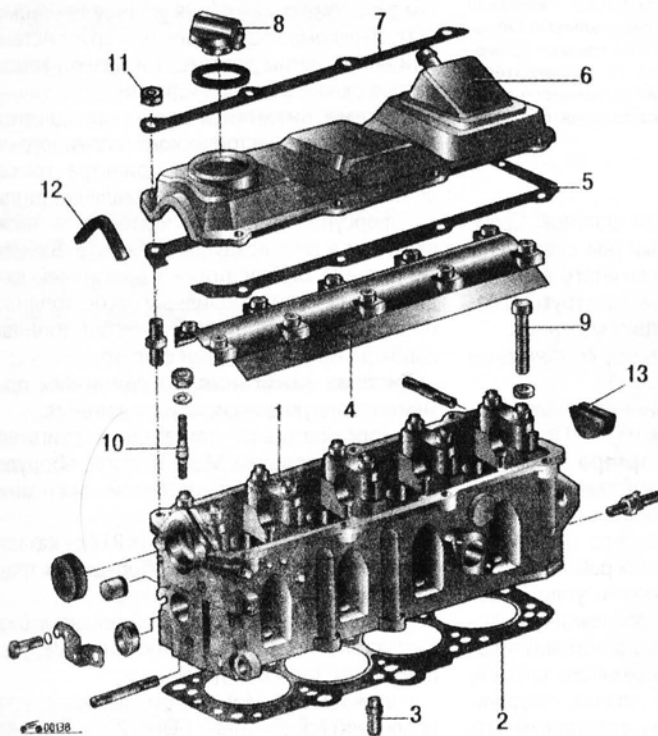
Головка блока цилиндров двигателей SOHC: 1 - головка блока цилиндров; 2 - прокладка головки блока цилиндров; 3 - направляющая втулка клапана; 4 - маслоотражатель; 5 - прокладка крышки головки блока цилиндров; 6 - крышка головки блока цилиндров; 7 - силовая полоска; 8 - пробка маслоналивной горловины; 9 - болт крепления головки блока цилиндров; 10 - шпилька крепления крышки головки блока цилиндров; 11 - гайка крепления крышки головки блока цилиндров; 12 - передняя прокладка крышки головки блока цилиндров; 13 - заглушка
